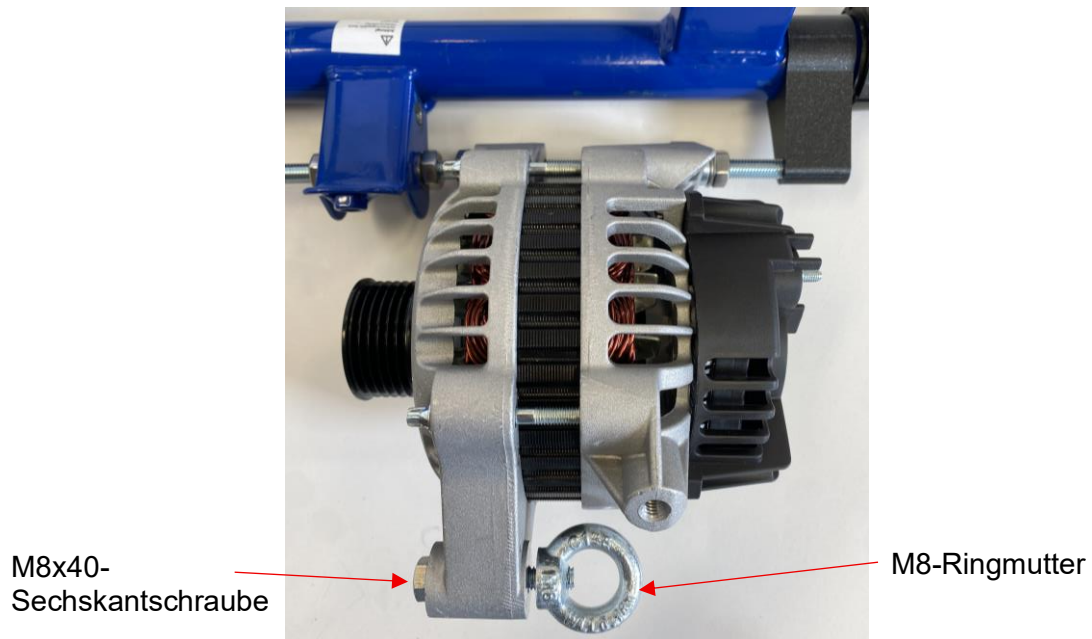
Montage der Ringmutter an der Lichtmaschine
